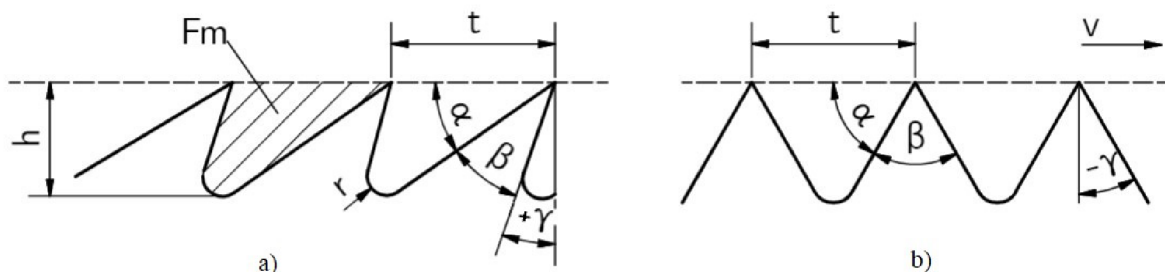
Dláto (a) a broušící papír (b) [22].
